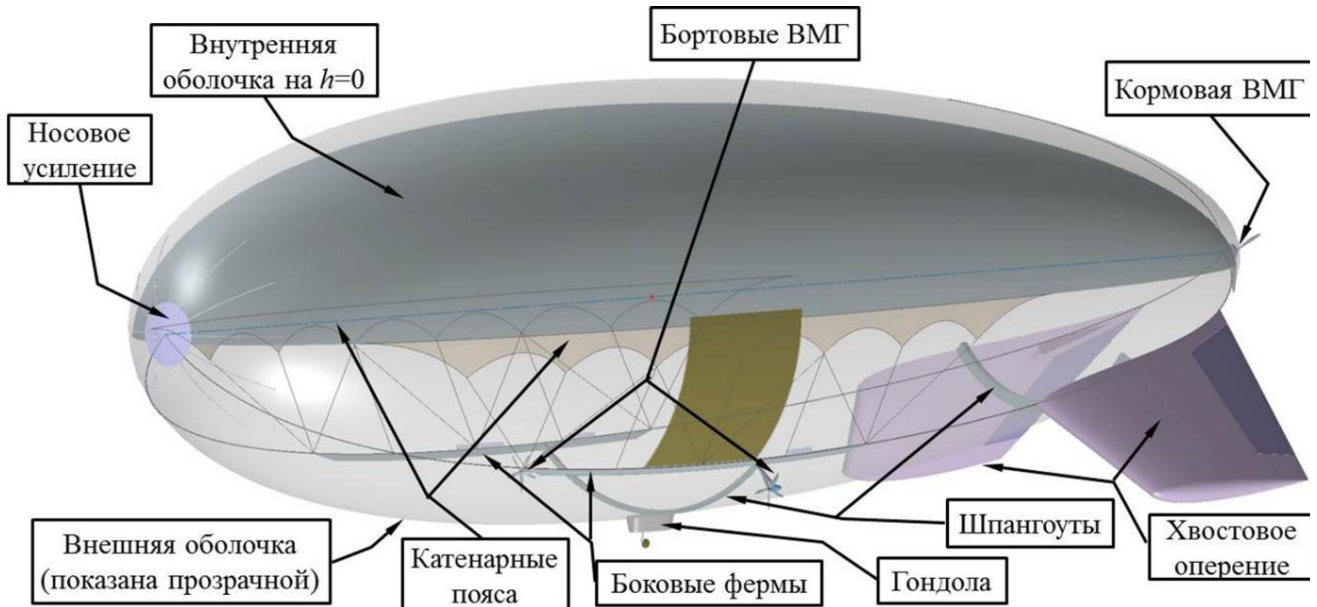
Конструктивно-силовая схема и компоновка ВД для варианта 2 минимальной размерности
